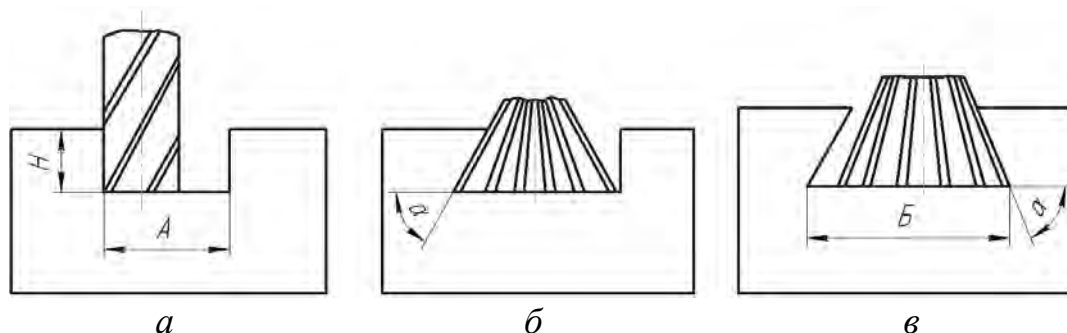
Фрезерование паза типа «ласточкин хвост» вертикальным шпинделем: а - формообразование прямого паза концевой прямой фрезой; б, в— формообразование поверхностей под углом  $\alpha$  концевой угловой фрезой
